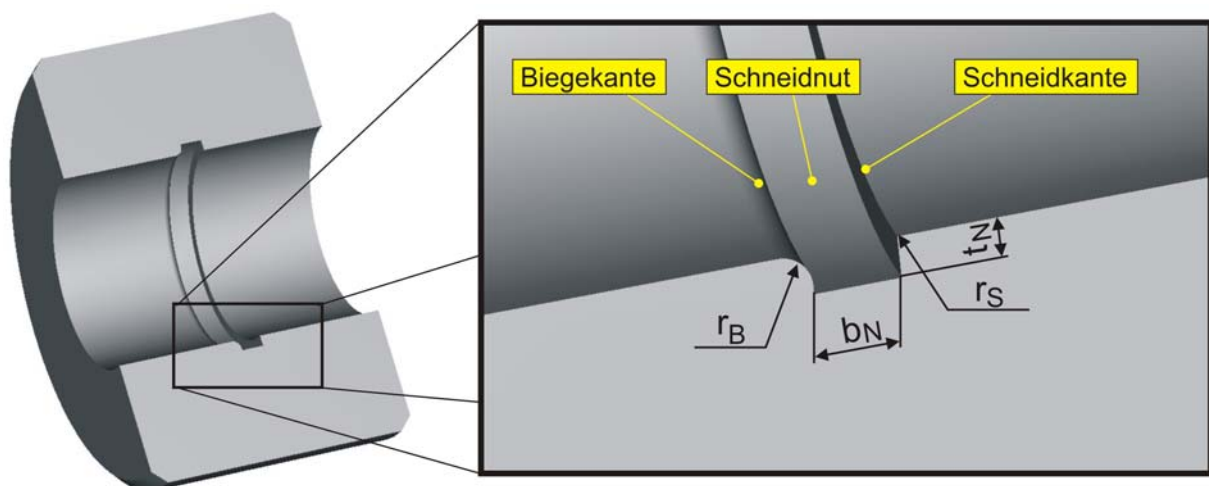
Geometrische Kenngrößen am Werkzeug für das Innenhochdruck-Einfachabschneiden
